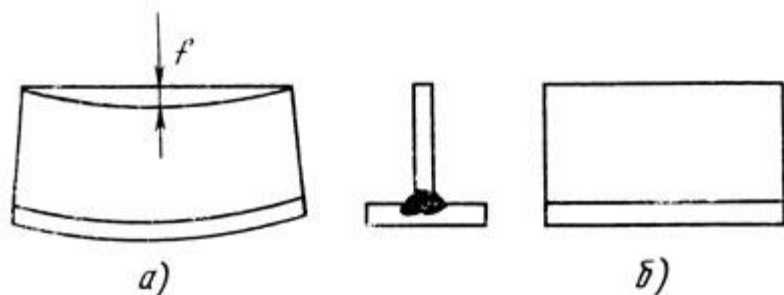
Обратный выгиб элемента тавра: а - сборка тавра с обратным выгибом f ; б - форма тавра после сварки
